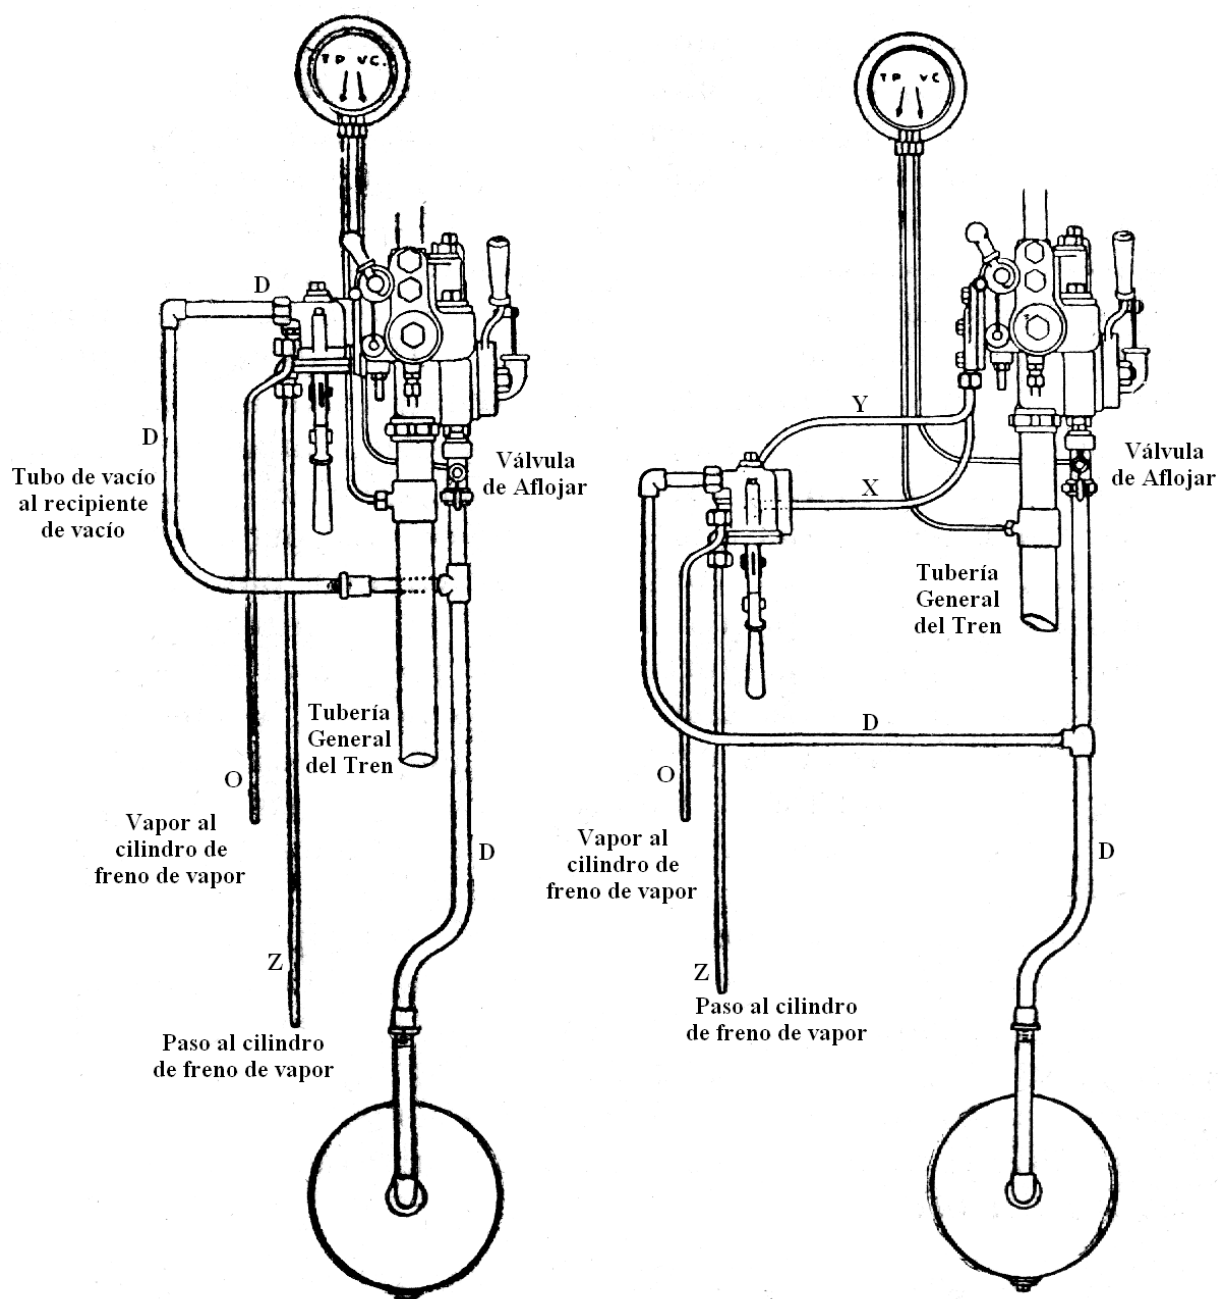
Dos disposiciones del freno a vapor combinado con el freno de vacío Gresham Super Dreadnought
